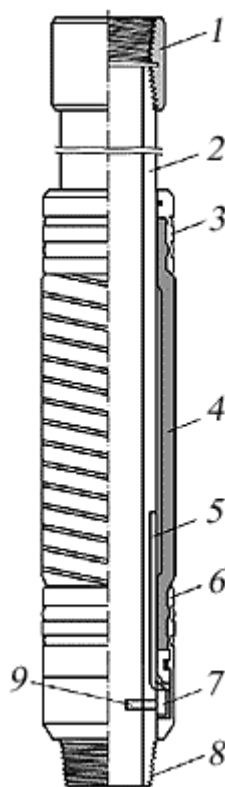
Пакер типа ПЗГ: 1 – муфта обсадной колонны; 2 – корпус; 3 – подвижный обжимной стакан; 4 – уплотнительный элемент; 5 – канал для подвода жидкости; 6 – неподвижный обжимной стакан; 7 – узел клапанный; 8 – резьба обсадных труб; 9 – полый срезной штифт
